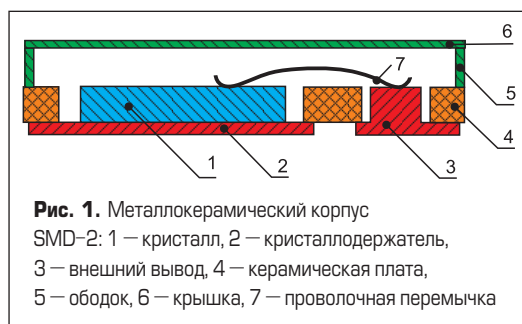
Металлокерамический корпус SMD-2: 1 — кристалл, 2 — кристаллодержатель, 3 — внешний вывод, 4 — керамическая плата, 5 — ободок, 6 — крышка, 7 — проволочная перемычка
